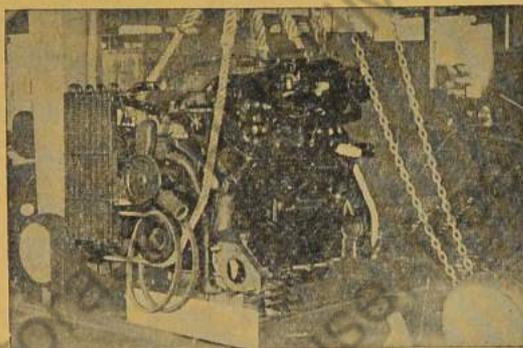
Motor mit Kupplungsgehäuse aus Fahrzeug herausheben
